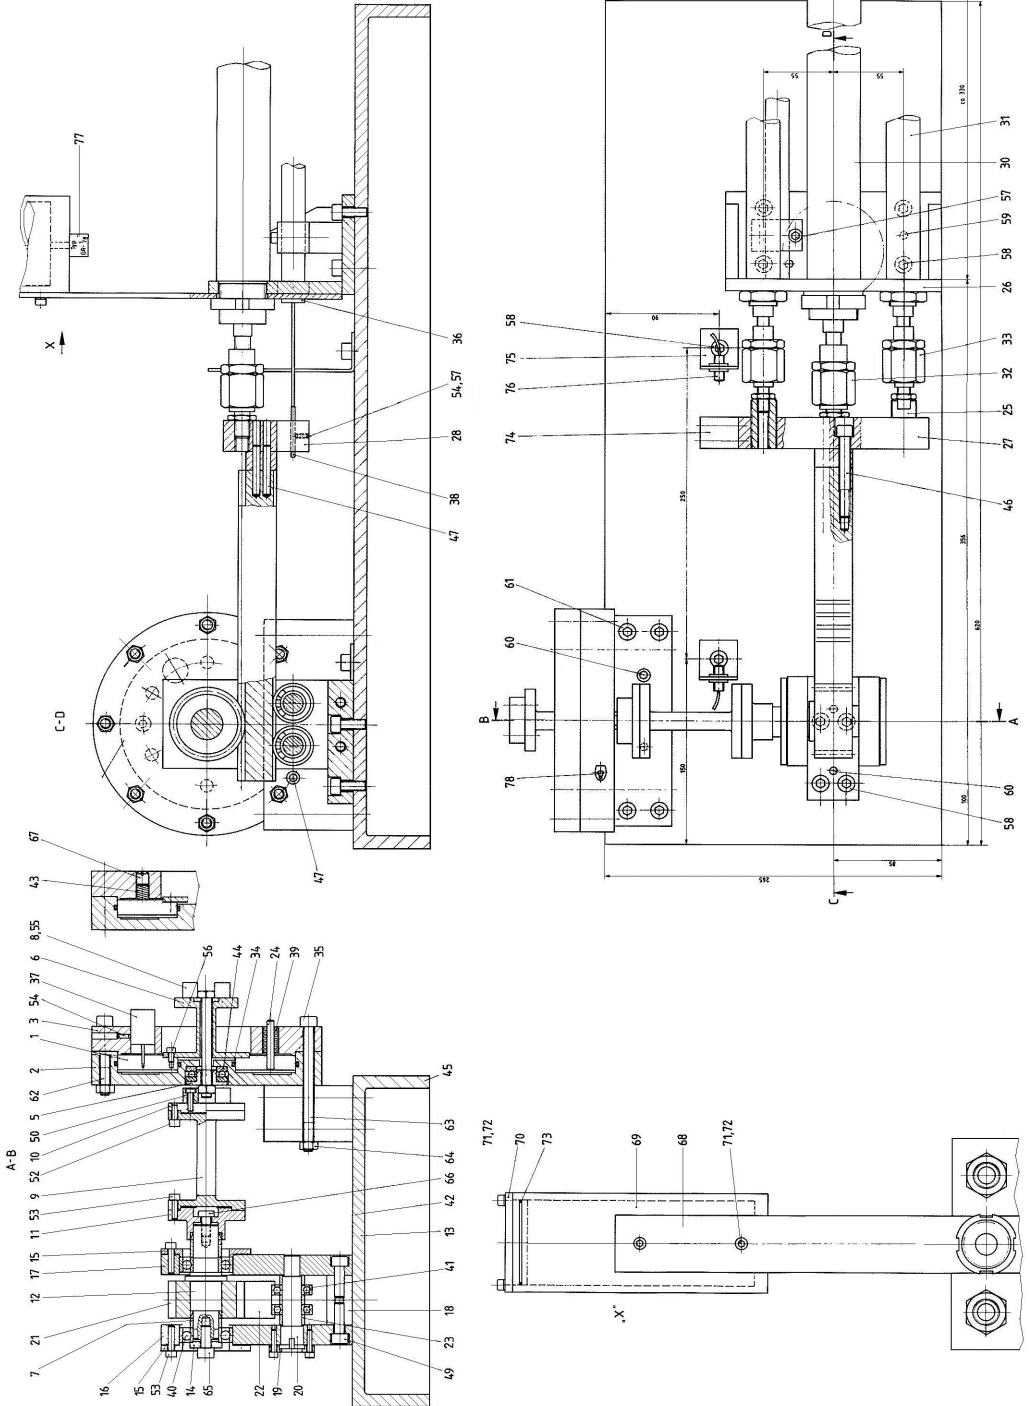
Ausführung einer Füge/Lösevorrichtung für Schrauben/Muttern
